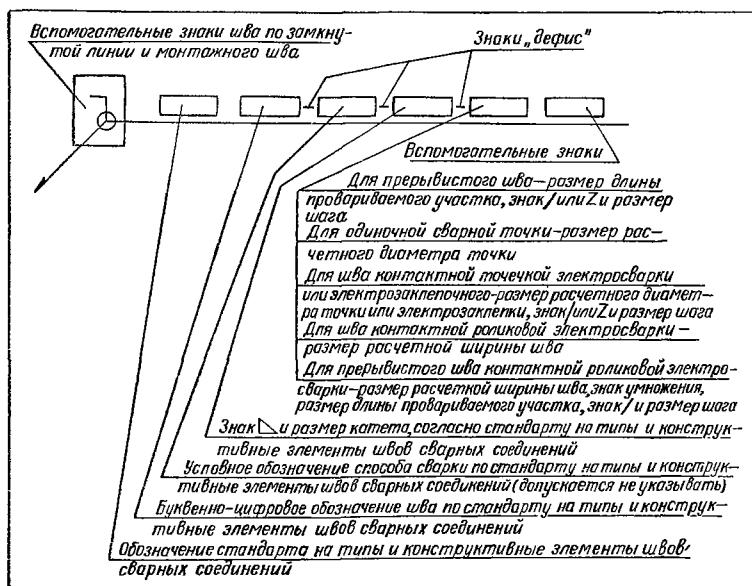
Структура условного обозначения стандартного шва или одиночной сварной точки
